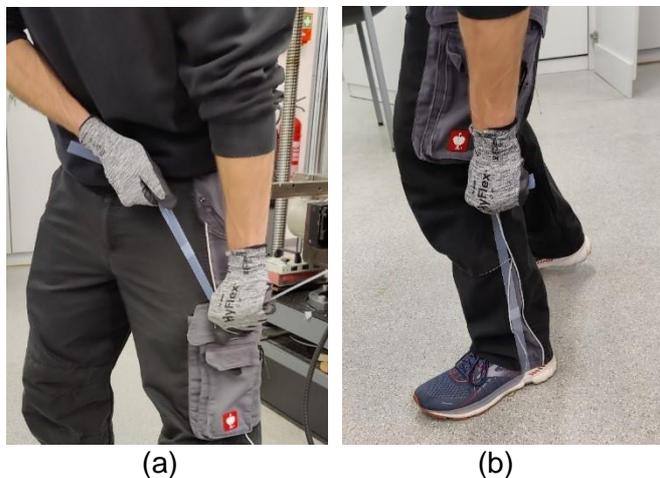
Durchführung einer manuellen Zug- bzw. Abschälprüfung; (a) Beidseitig manuelles Abziehen, (b) Einseitig am Boden fixiert, Fotos: UDE/IML
